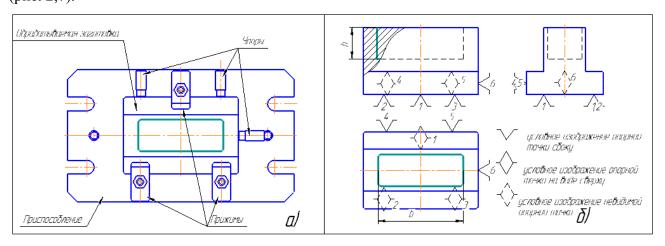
Полное базирование заготовки (1, 2, 3, 4, 5, 6 – опорные точки) а) установка заготовки по плоскости и двум сторонам; б) схема базирования
